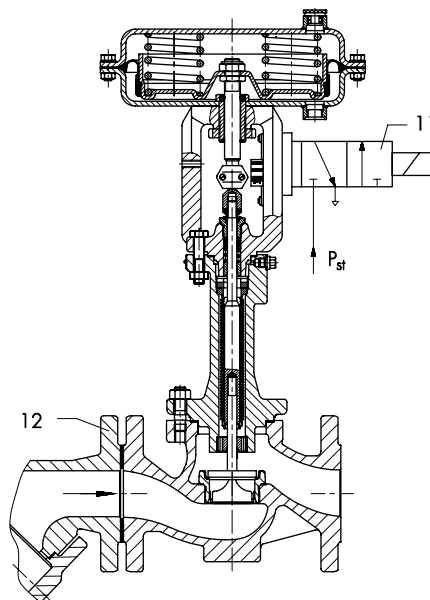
· Пневматический регулирующий и быстро закрывающийся клапан тип 3241-1-газ
